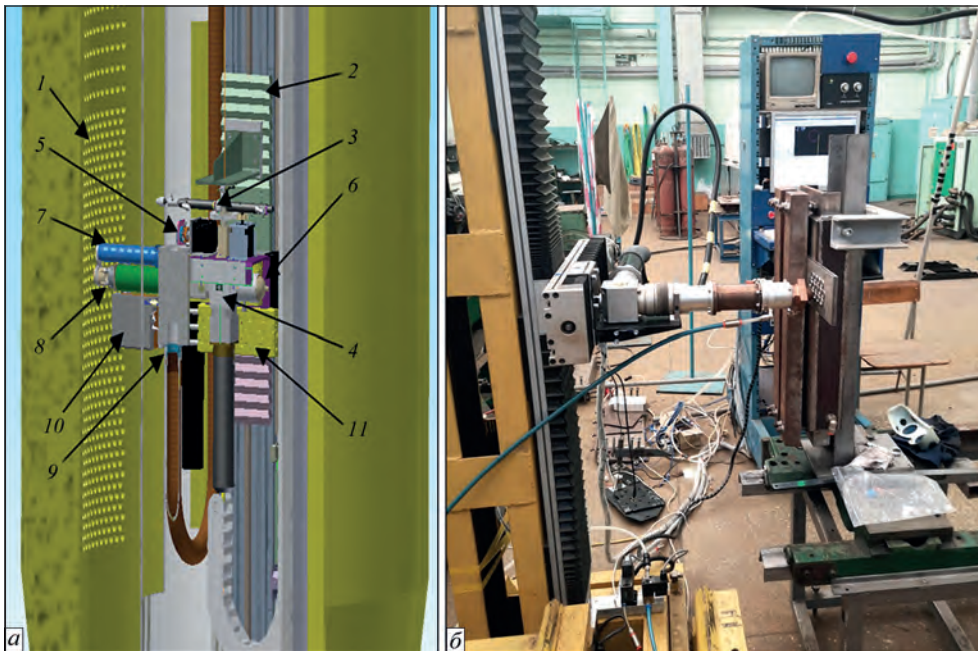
3D-модель (а) та діючий макет (б) обладнання для лазерного дистанційно керованого вварювання заглушок колектора парогенератора: 1 – стінка колектора; 2 – каретка маніпулятора; 3 – автоматизований пристрій встановлення заглушки; 4 – корпус оптики лазерної зварювальної головки; 5 – сканатор; 6 – відеокамера; 7 – гофрурукав для видалення випаровувань; 8 – пристрій газового захисту; 9 – система фільтрації; 10 – датчик визначення положення місця зварювання; 11 – привід датчику визначення положення місця зварювання
